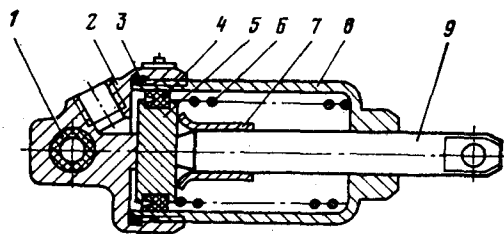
Пневматический цилиндр 30×25 отключения подачи топлива:
